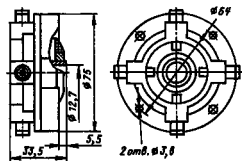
Габаритные и установочно-присоединительные размеры тахогенератора ТП80-20-0,2
